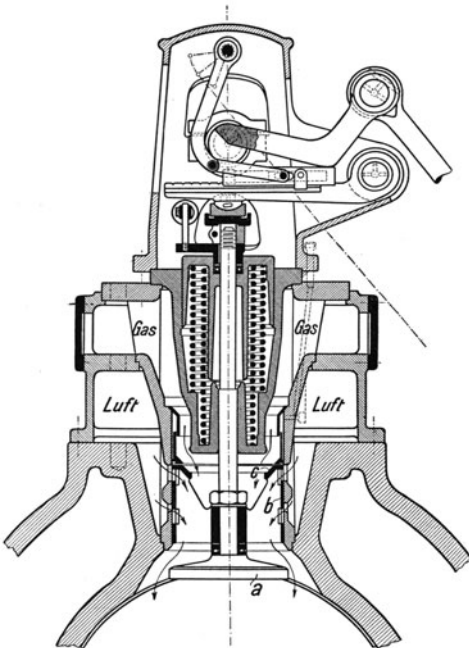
Einlaßsteuerung der MAN für Großgasmaschinen.
